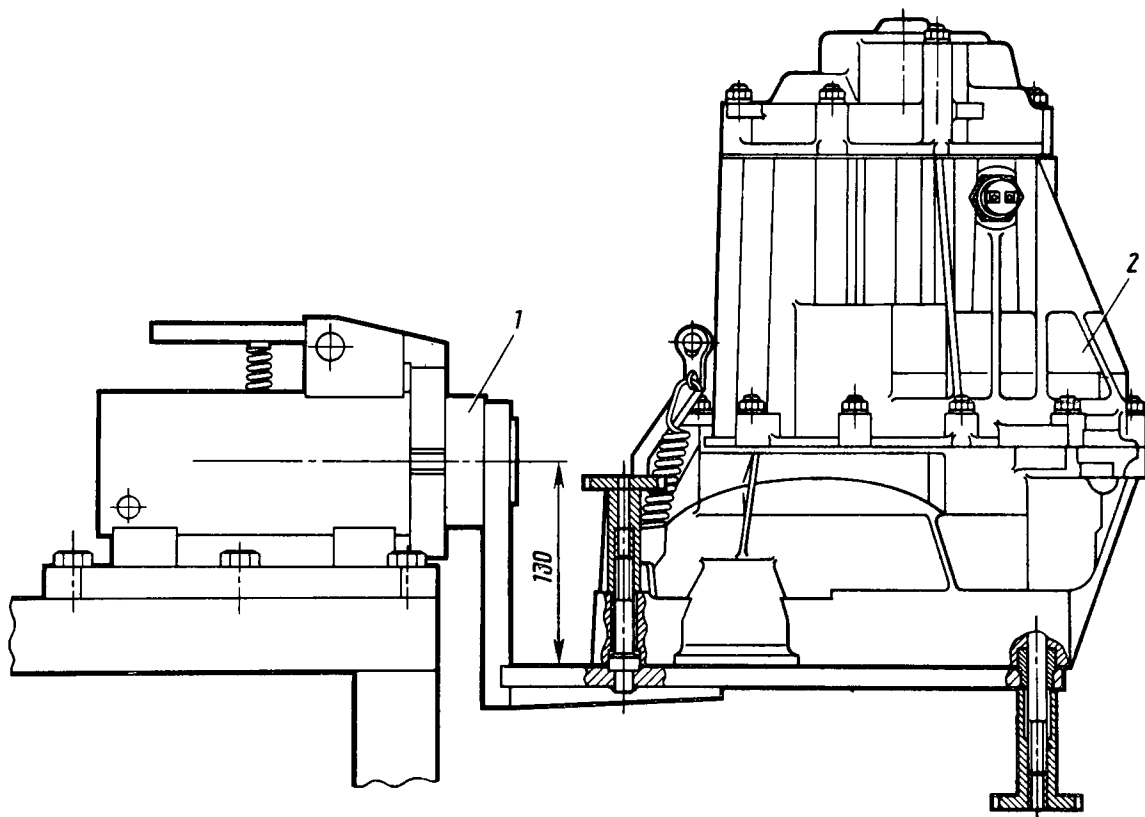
Коробка передач, установленная на приспособление для разборки и сборки:
